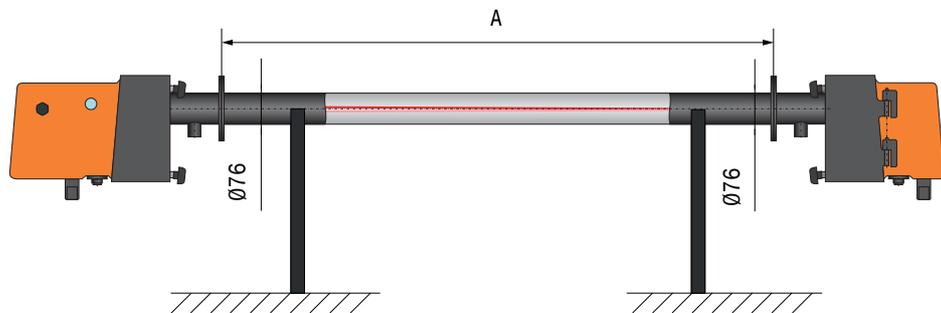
Montaje del reflector DHT-R5x en el caballete de ajuste
